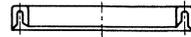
Schlechte Form eines Nutringstulps. Abgerundete Böden (Abb. 7) sind für die Lederverarbeitung günstiger als die eckige Form
